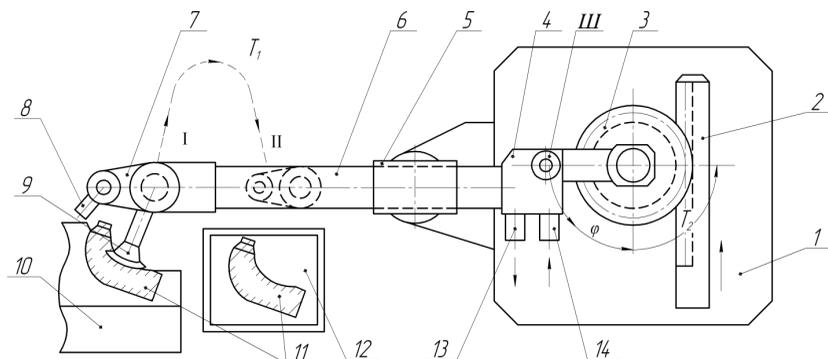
Манипулятор для извлечения стержней из стержневых ящиков: 1 – основание; 2 – рейка; 3 – зубчатое колесо; 4 – кривошип; 5 – направляющая втулка; 6 – рука манипулятора; 7 – поворотная кисть; 8 – сопло; 9 – вакуумная присоска; 10 – стержневой ящик; 11 – стержень; 12 – стержневая плита; 13 – штуцер для создания вакуума в присоске; 14 – штуцер подачи сжатого воздуха
